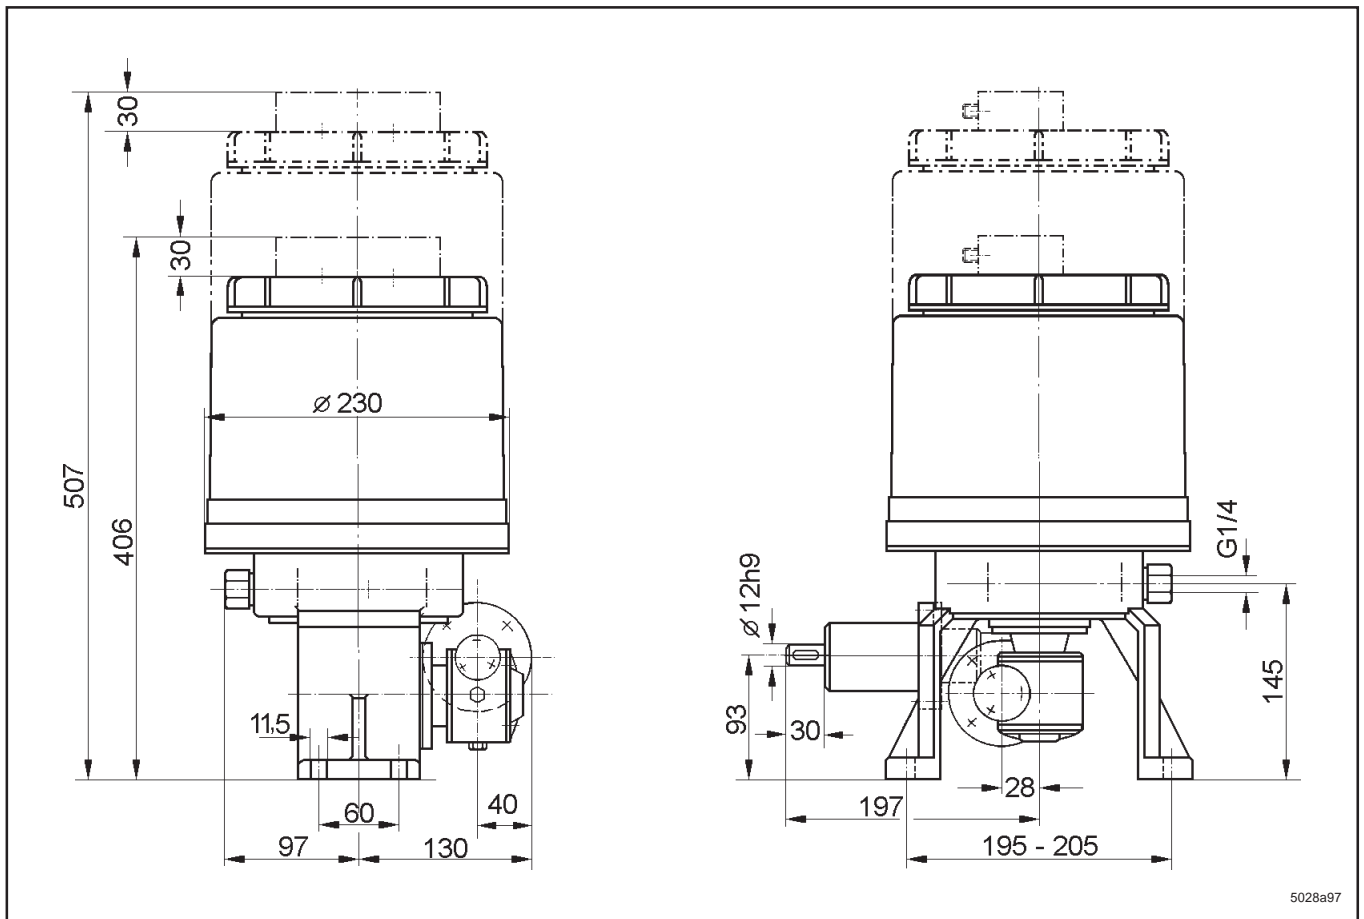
Maßzeichnung für Pumpe P205, 2-stufiges Getriebe, 4/8l Kunststoffbehälter, freies Wellenende
